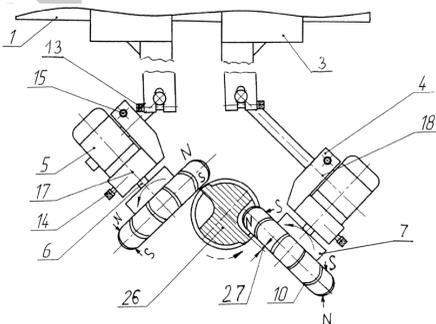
Схема применения устройства при обработке спиральной поверхности или спиральной канавки детали на горизонтально-фрезерном станке, оснащённом поворотным столом
